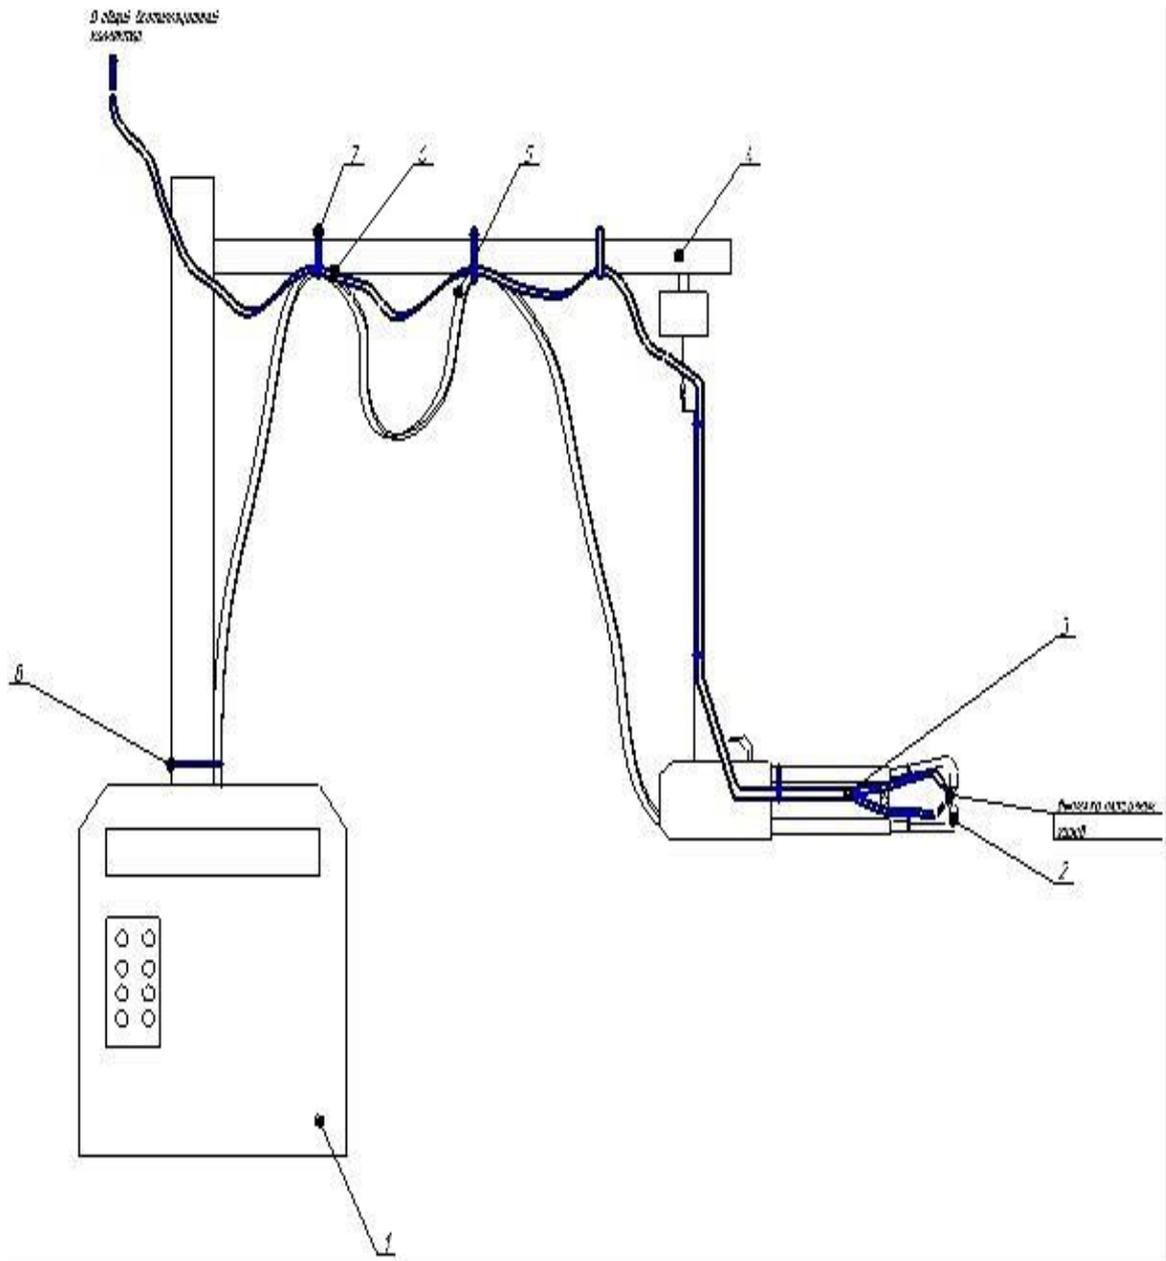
Местная вентиляция для машин точечной контактной сварки: 1- силовой шкаф (источник питания); 2- сварочные клещи; 3 – вытяжной канал; 4 – поворотная консоль; 5 – силовые кабели; 6 – вытяжной шланг; 7 – подвижные направляющие ролики; 8 – диэлектрические крепежи.
